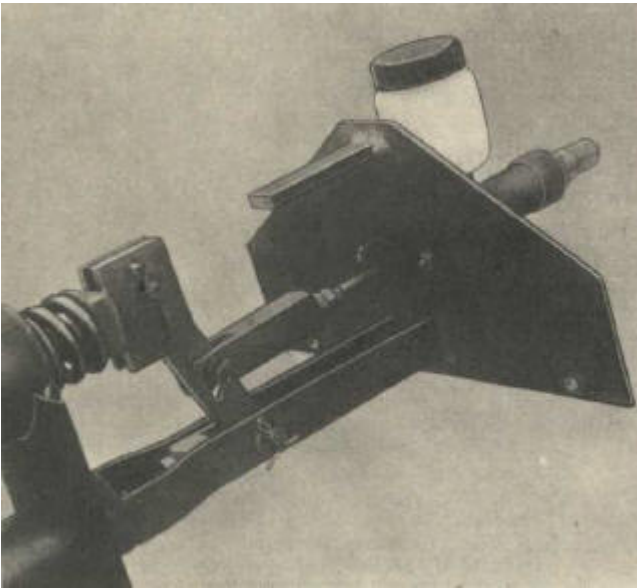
Hauptbremszylinder, am Stegblech des Auflaufschubstückes befestigt
